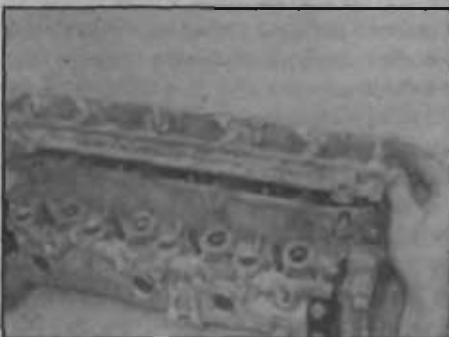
Снятие корпуса подшипников распределительного вала
